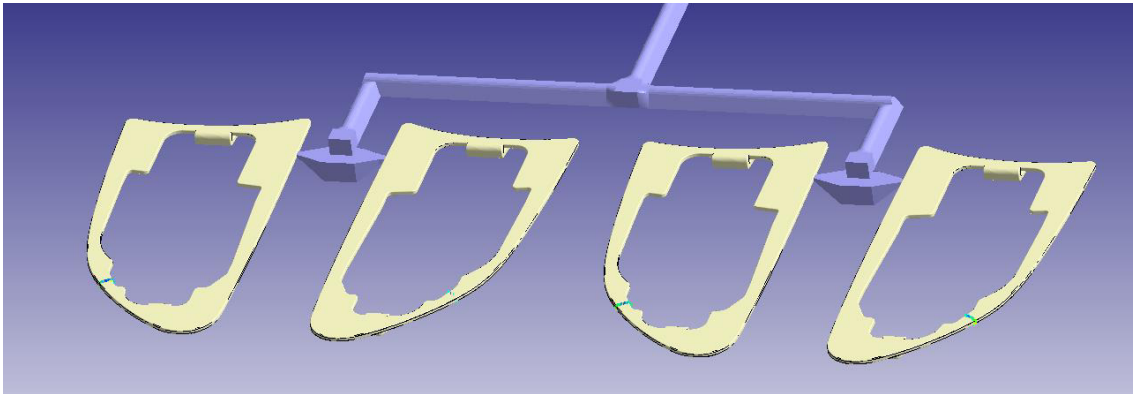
Localização das linhas de soldadura das moldações do Projeto B
